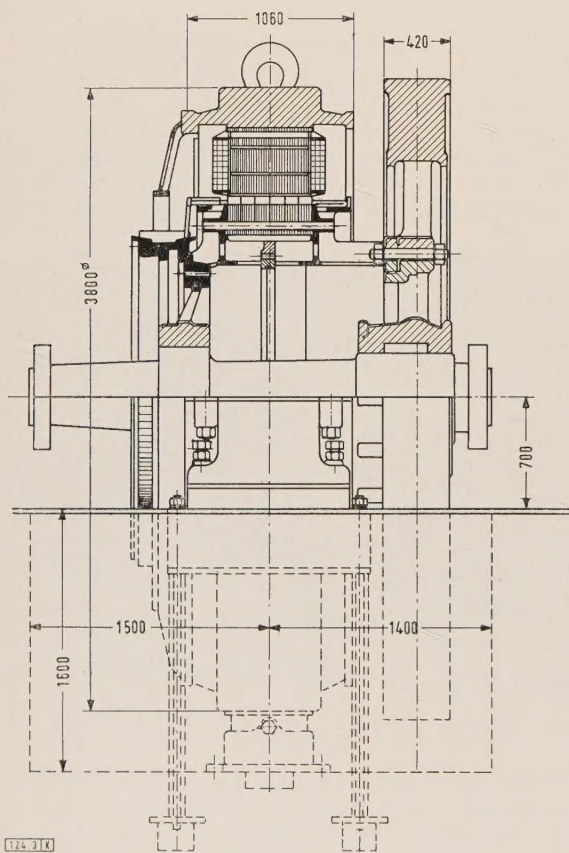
Gleichstrommaschine der Maschinenfabrik Leopoldau (1900), Schnittzeichnung.
